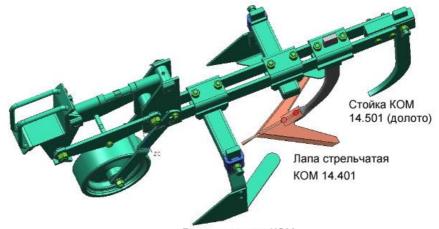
Общий вид культиватора КРН-8,4 А
